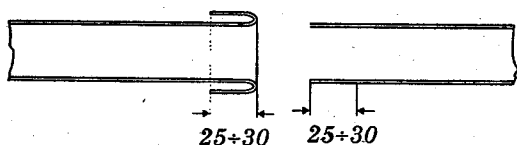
Участки, подвергаемые шероховке перед стыковой камерой
